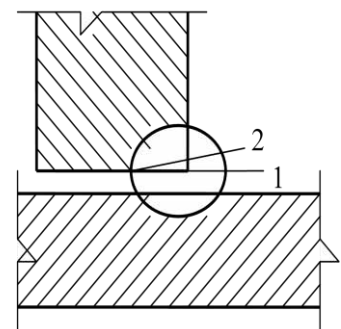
Схема розрахункових перерізів зварного з'єднання з кутовим швом
